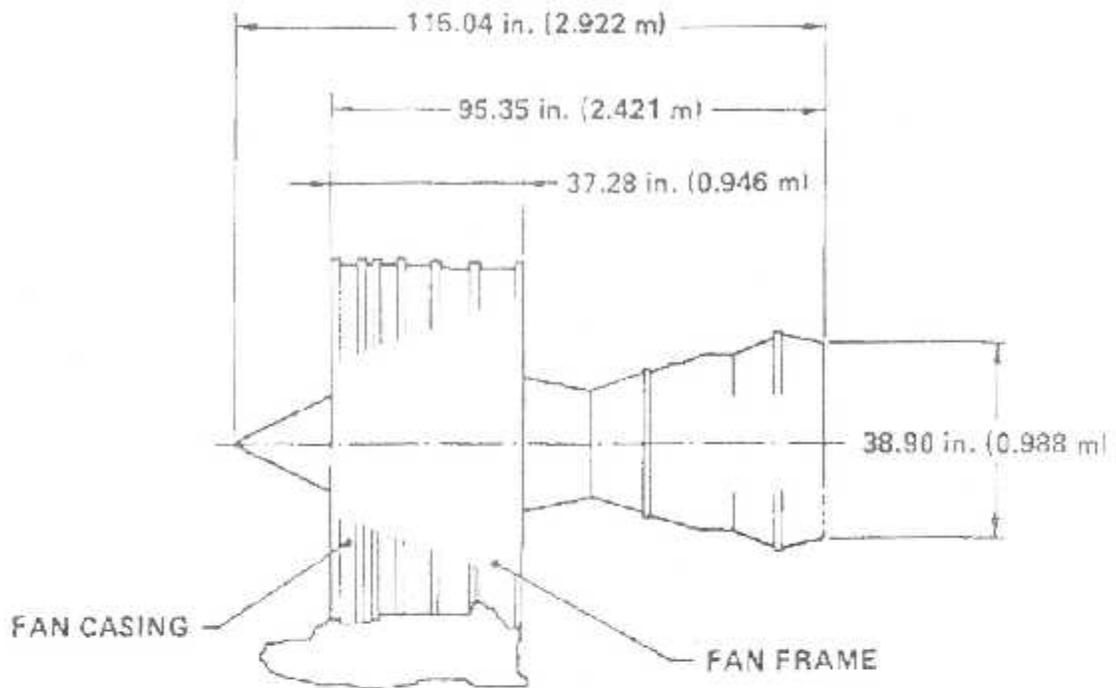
DIMENSIONS PRINCIPALES EXTERNES DU MOTEUR CFM56-5B
